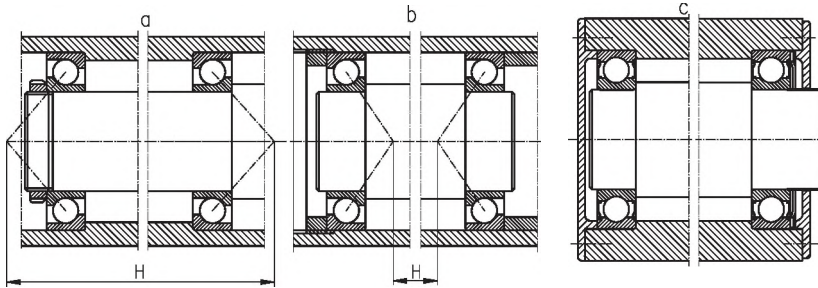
Подшипниковые узлы с фиксированными и свободными подшипниками
